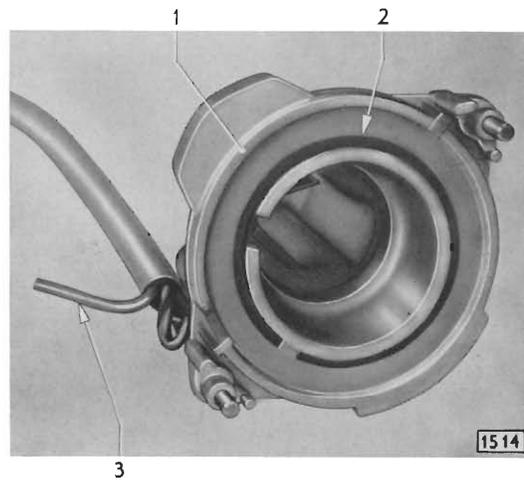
Gelenkteil auf Blinkerschaltergehäuse mit Sicherungsring befestigt
